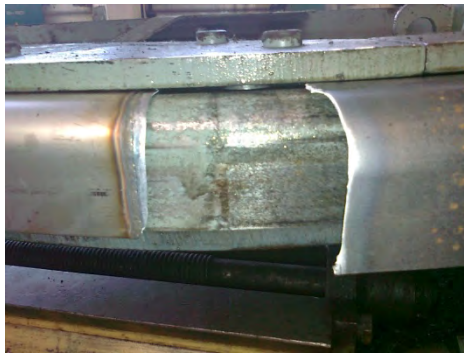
Разрыв сварного шва при гибке с растяжением дуг пассажирских вагонов из разнородных металлов
